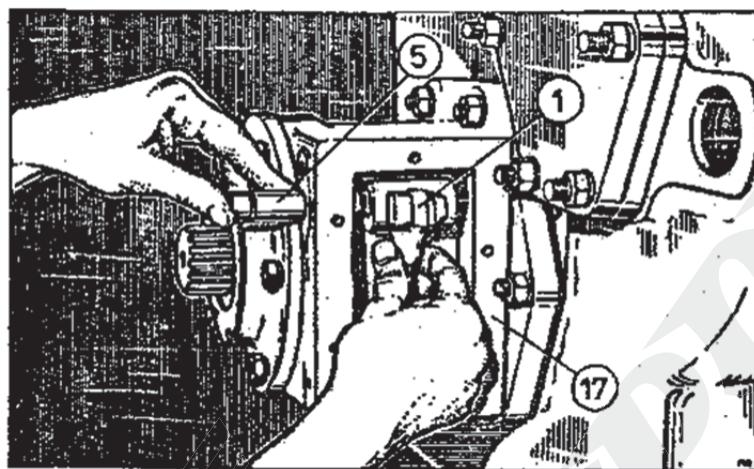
Установка вилки 1 в канал переключающего блока и установка валика 5 через отверстие в корпусе 17 а отверстие в вилке 1.
